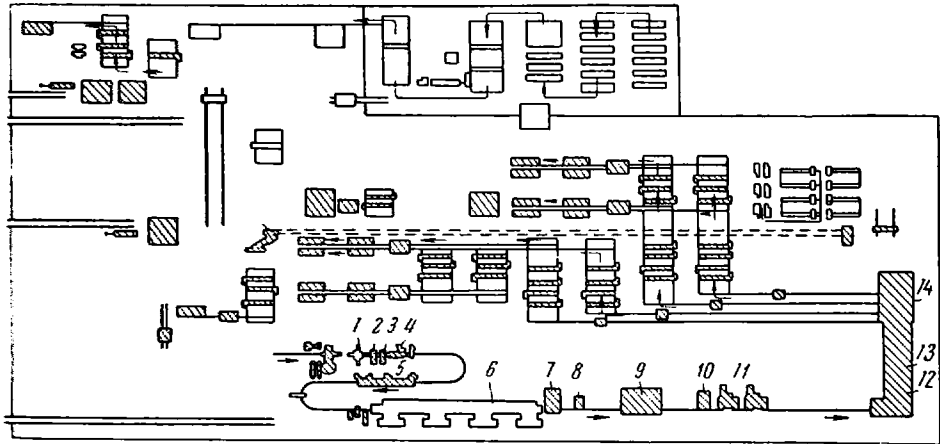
Схема расположения оборудования агрегата непрерывной печной сварки труб
